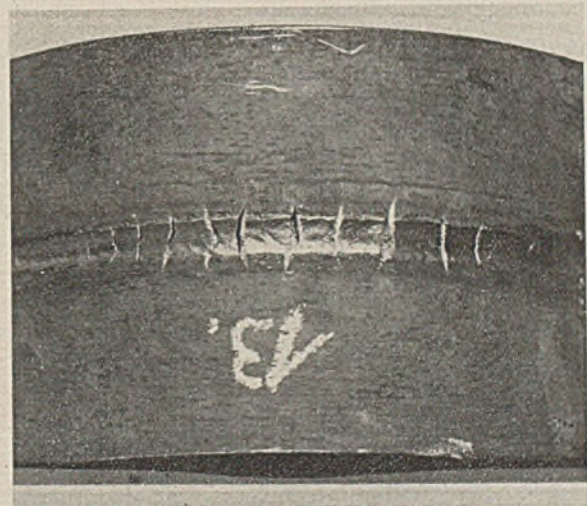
Aufschweißbiegeprobe mit zahlreichen Anrissen.
